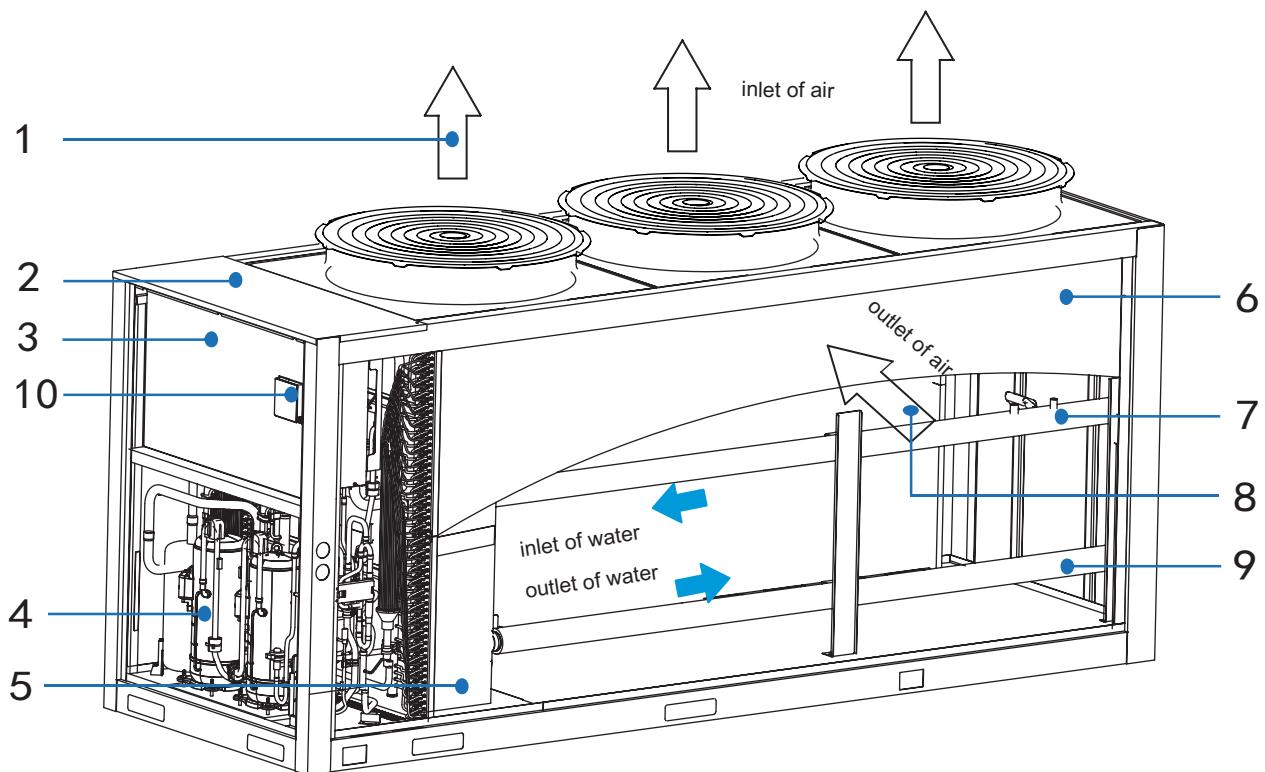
Componenti principali dell'unità KEM-90 DNS3
